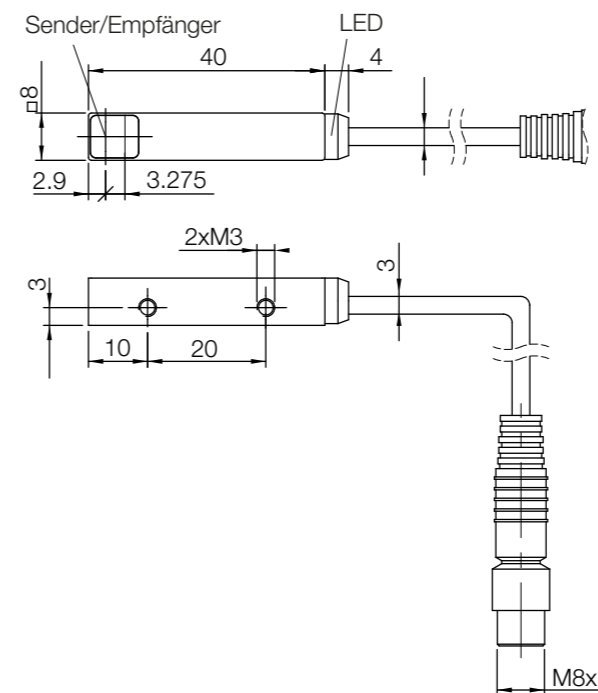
Abmessungen BOS Q08M-...-00,2-S49
